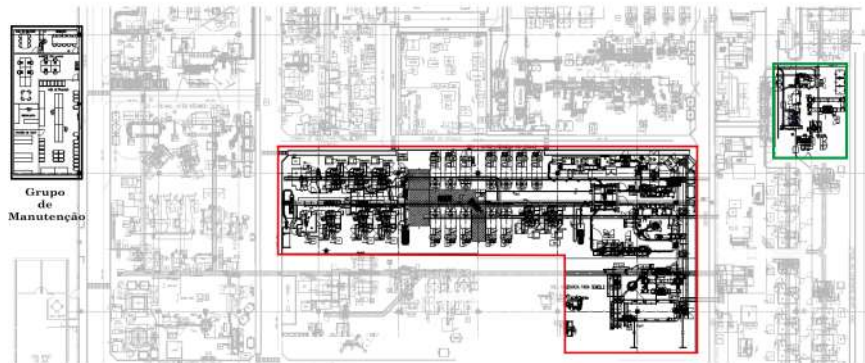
Planta da área de fabrico do Cárter Intermédio.
